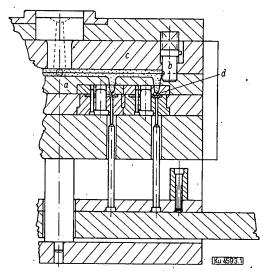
Spritzgußwerkzeug mit Anguß-Abreißvorrichtung
